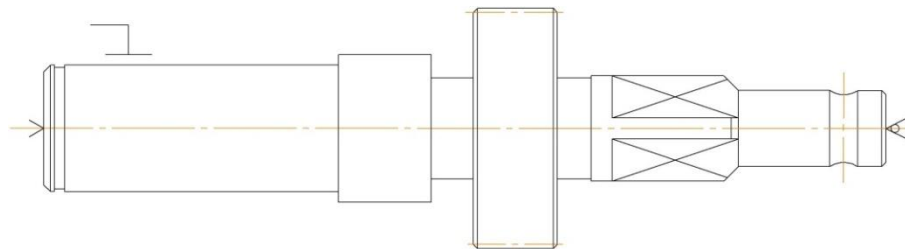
Ескіз обробки деталі на 025 операції.
